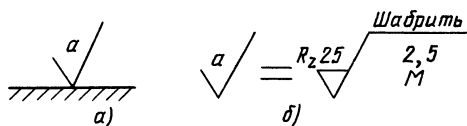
Упрощенное обозначение шероховатости на чертеже:
